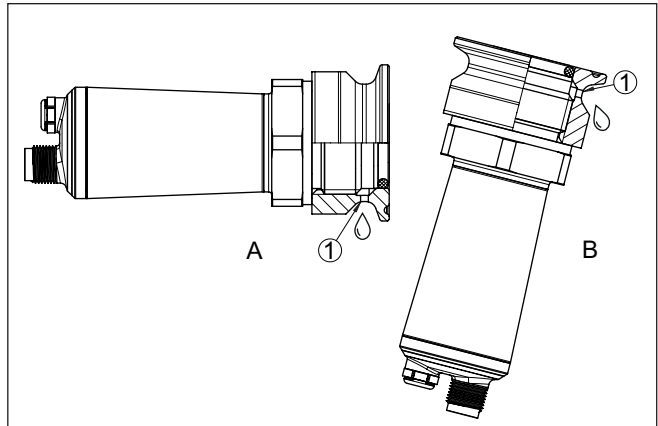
Ausrichtung des Einschweißstutzen
